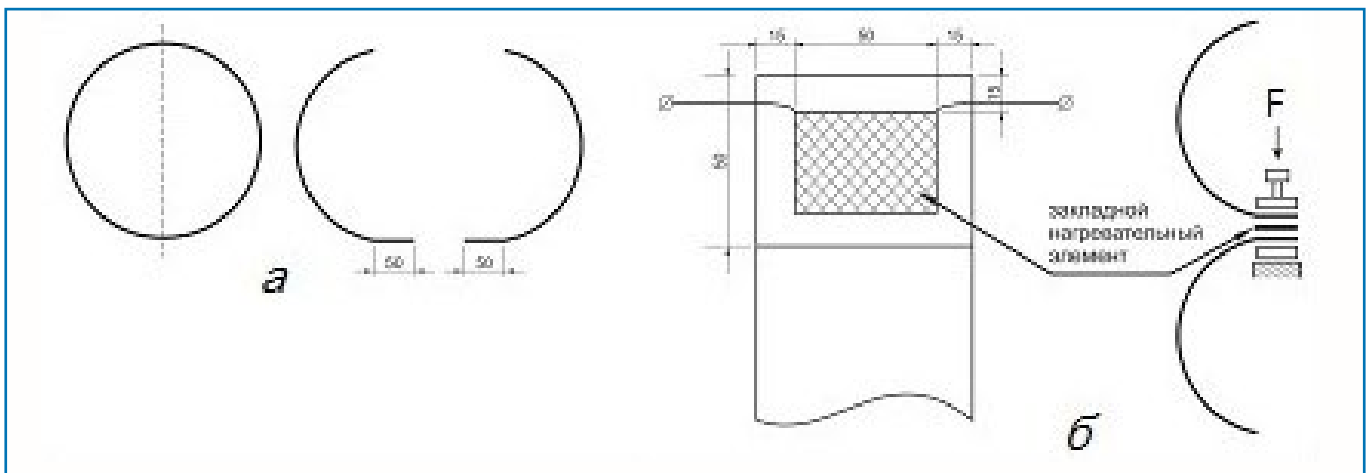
Схема образцов (а), подготовленных для последующей сварки с помощью ЗНЭ и проведения испытаний на расслаивание (б): F – усилие прижима.
